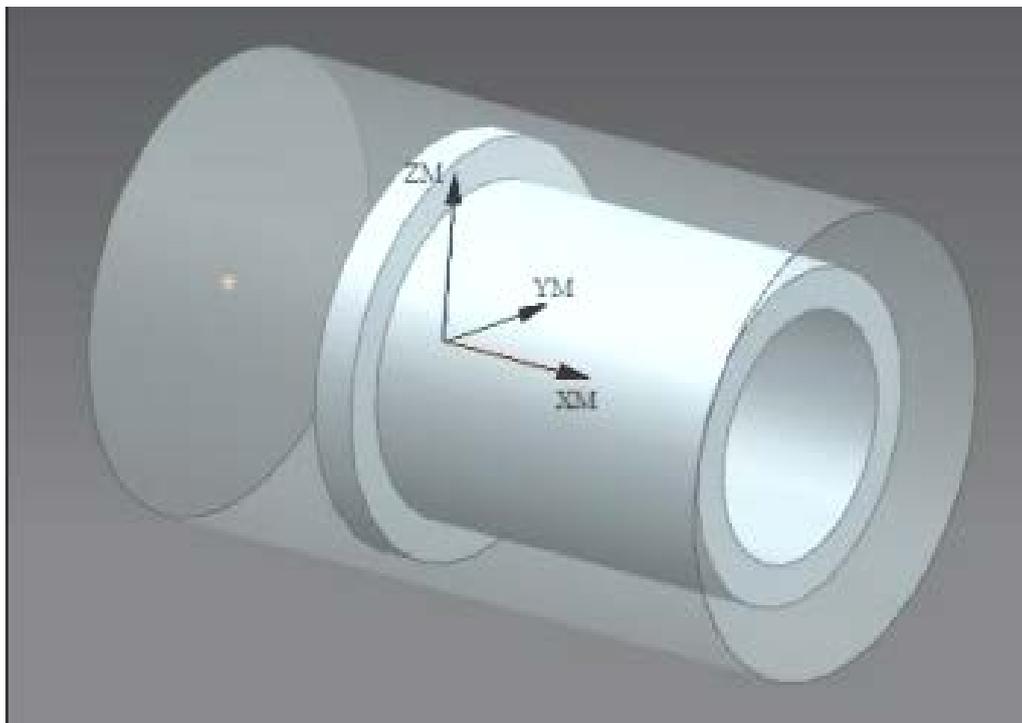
3D-модель детали после наложения на нее модели заготовки
